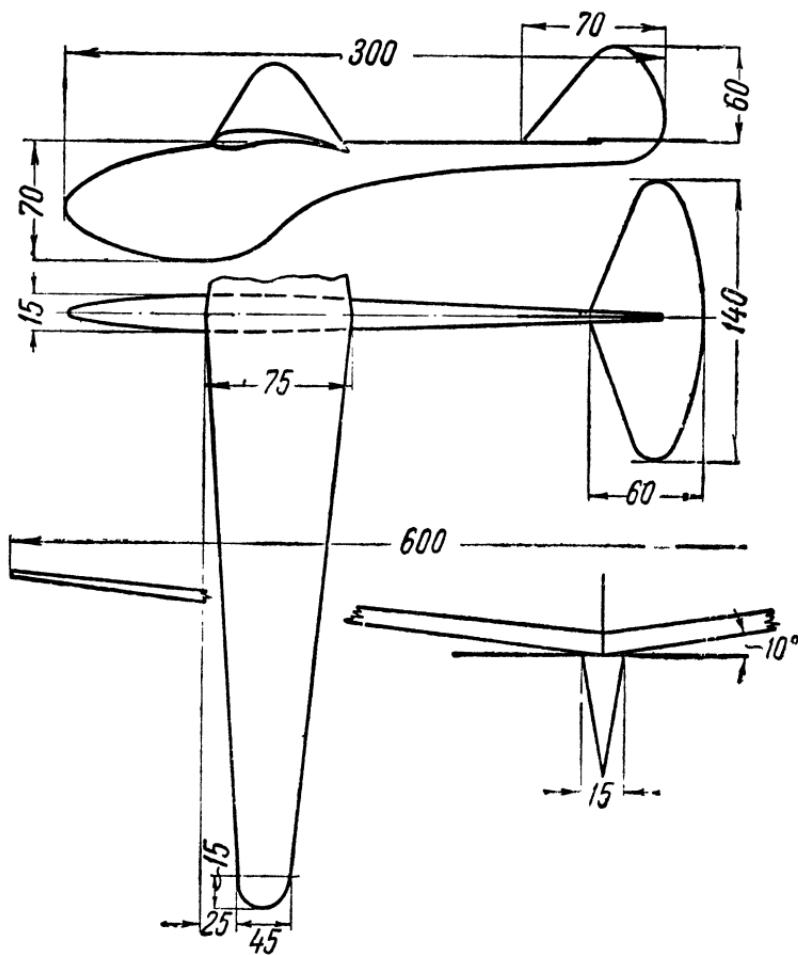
Рабочие чертежи деталей, из которых изготавливается модель:
